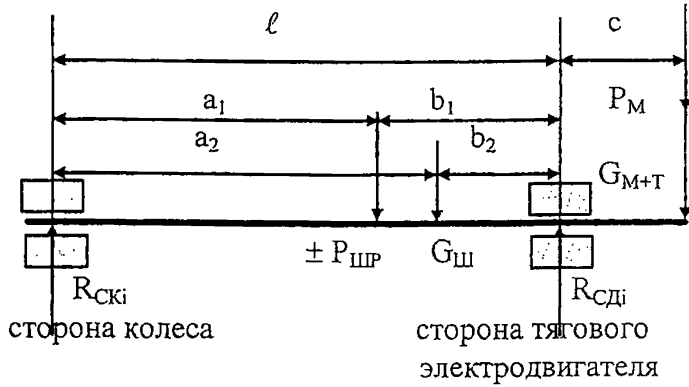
Схема для расчета нагрузок на подшипники ведущей шестерни
